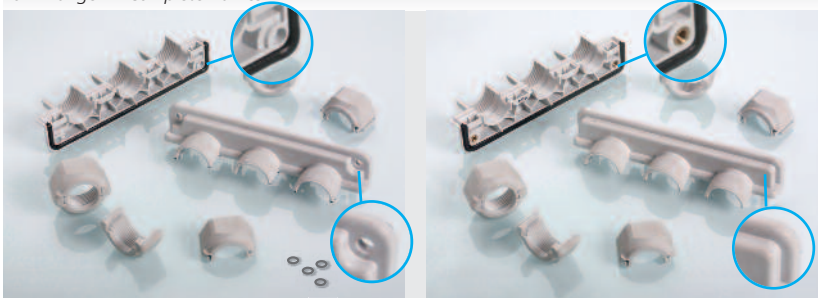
UNI FLANSCH™ mit Durchgangslöchern
